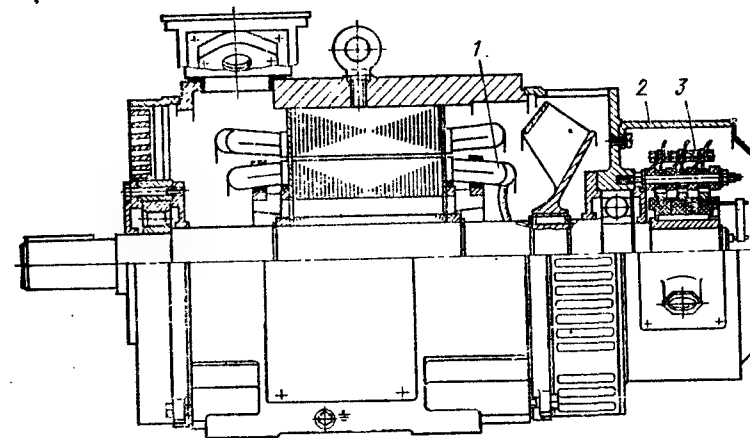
Асинхронный двигатель с фазным ротором 4АНК160.
